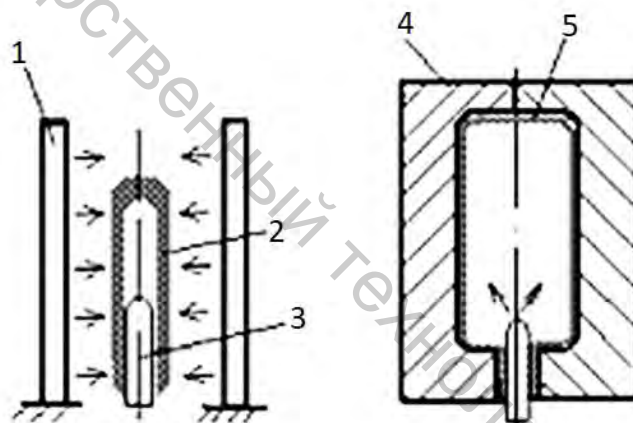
Схема формования изделий из инъекционной заготовки
